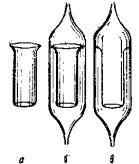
Изготовление внутреннего спая с применением "тарелочки": а — развертывание внутренней заготовки в виде "тарелочки"; б—введение внутренней заготовки в широкую трубку; в—готовый спай.
